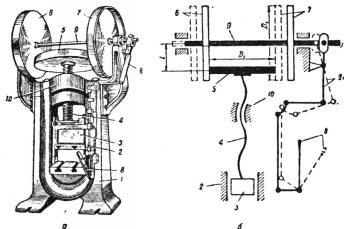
Фрикционный винтовой пресс с цилиндрическими колесами:
